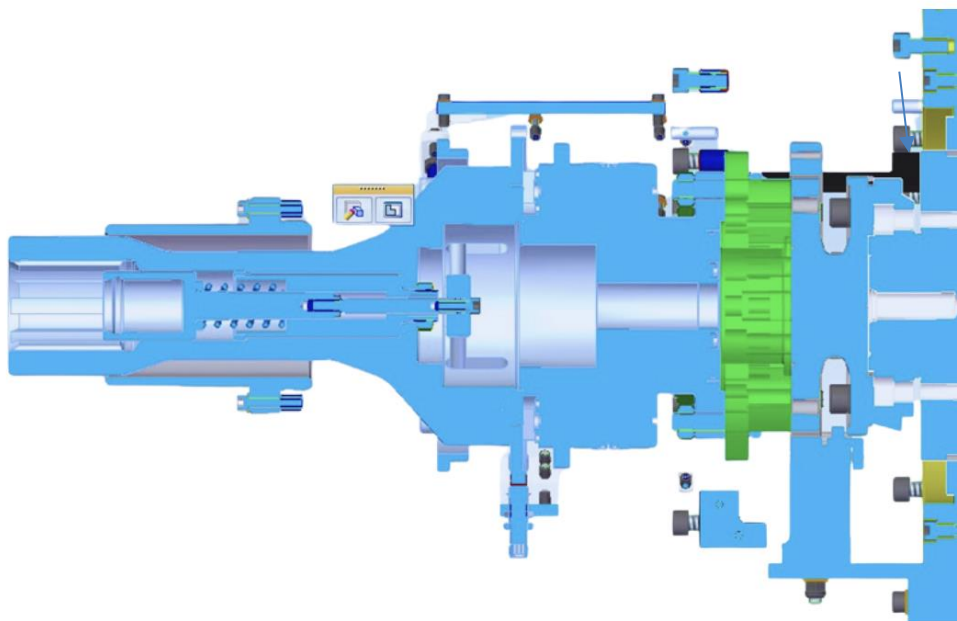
Sistema di trasmissione dall'assale alle dinamo
